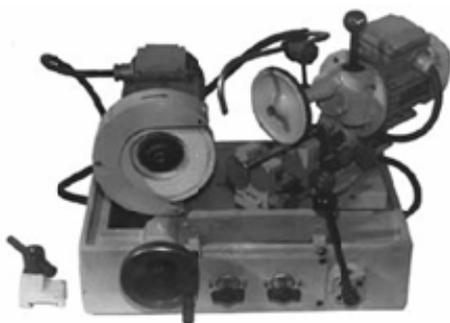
Установка для шлифовки фасок и торцов клапанов, мод. Р 186
